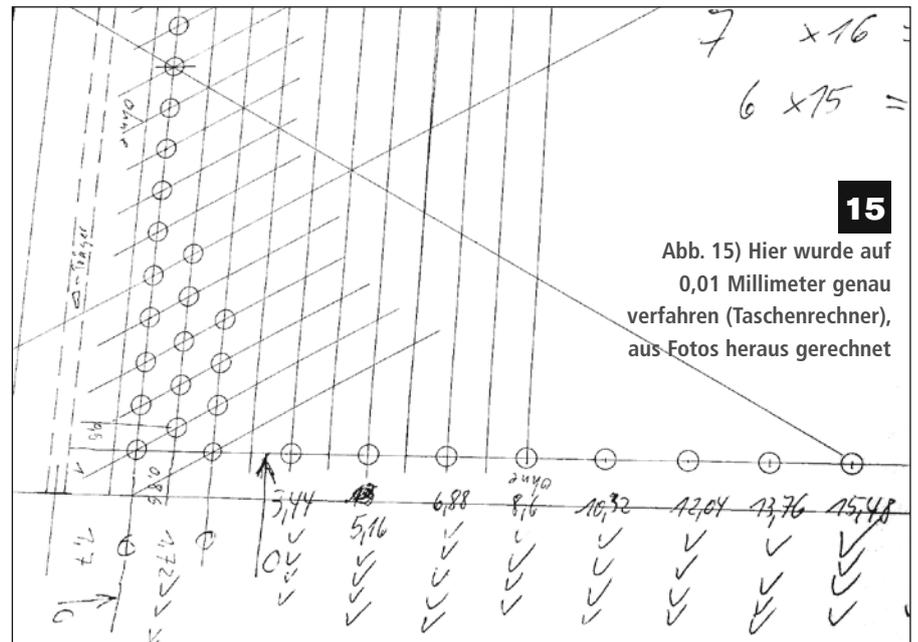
Hier wurde auf 0,01 Millimeter genau verfahren (Taschenrechner), aus-Fotos heraus gerechnet
